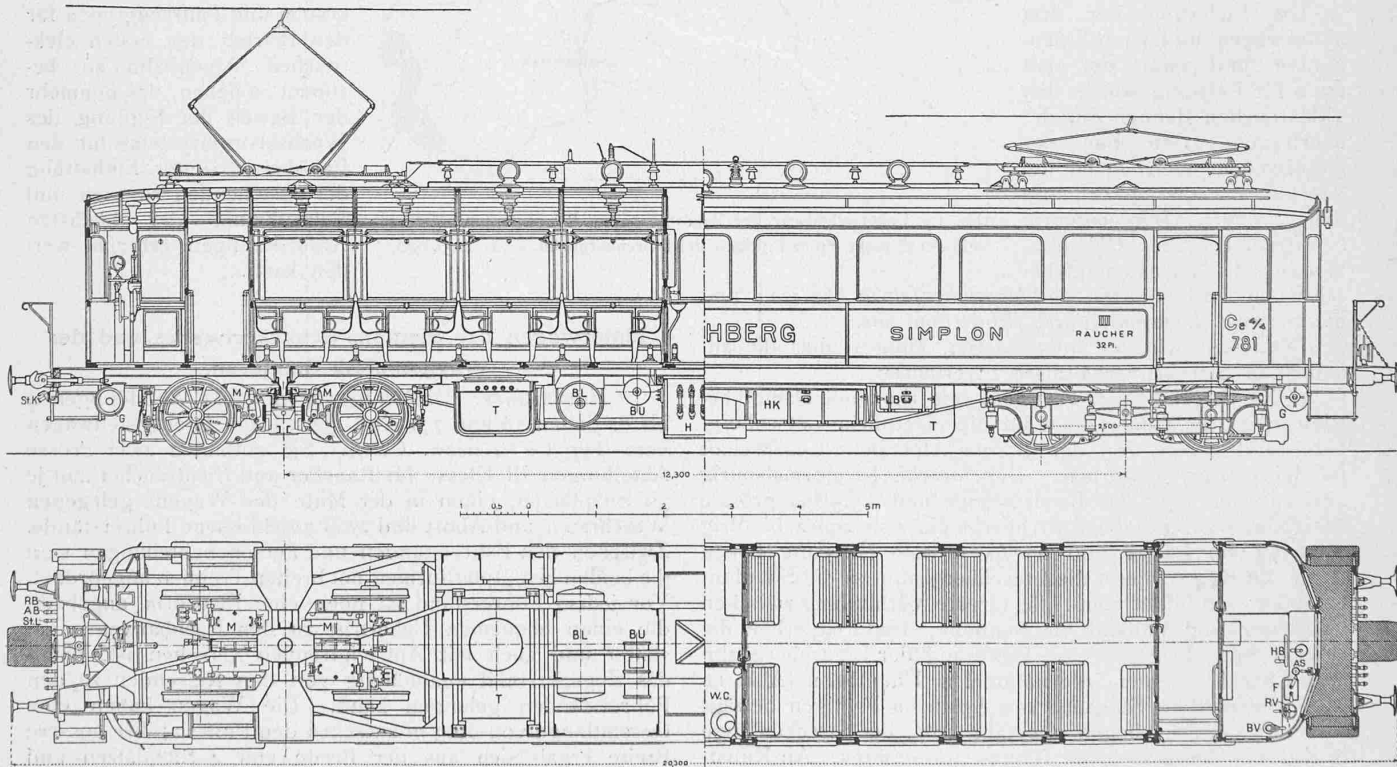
Ansicht, Draufsicht und Längsschnitt des Motorwagens. — Masstab 1:100.
